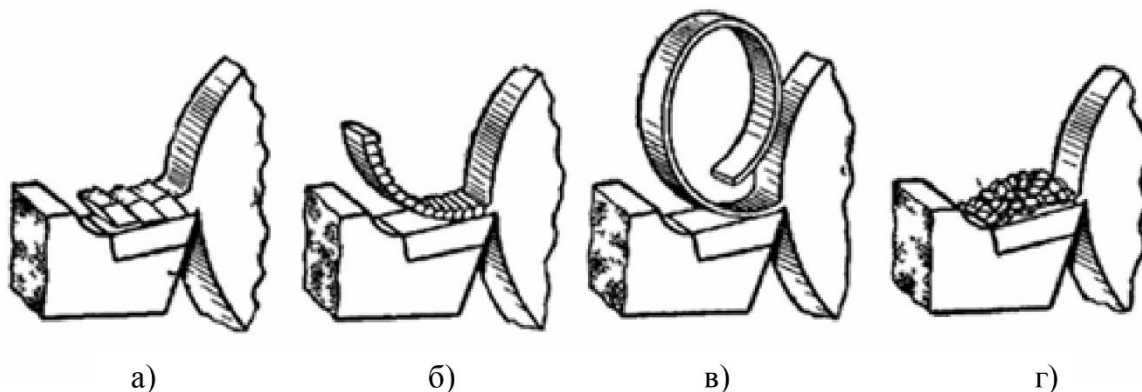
Типы стружек, образующихся при резании металлов: а – сливная; б - элементная; в – суставчатая; г – надлома [26-28]
